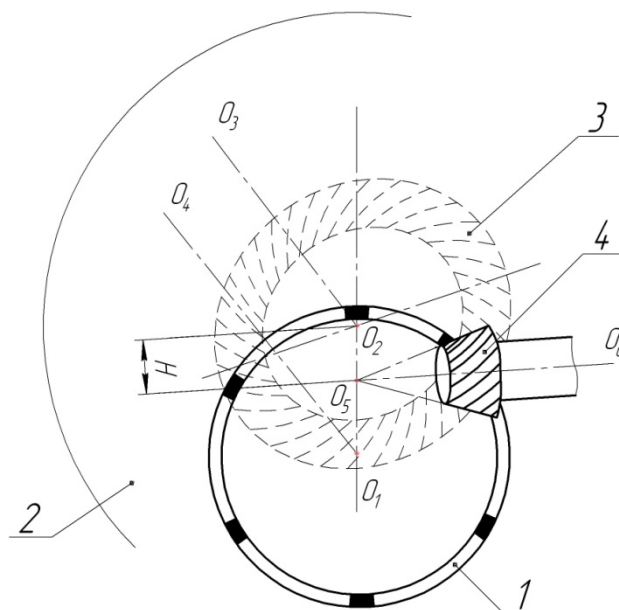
Схема установки режущего инструмента и заготовки при нарезании резцовой головкой гипоидных конических колес: 1 – резцовая головка; 2 – люлька; 3 – геометрическое плоское производящее колесо; 4 – нарезаемое гипоидное колесо; O_1, O_4 – ось вращения резцовой головки; O_2, O_3 – ось вращения люльки; O_5, O_6 – ось вращения заготовки
